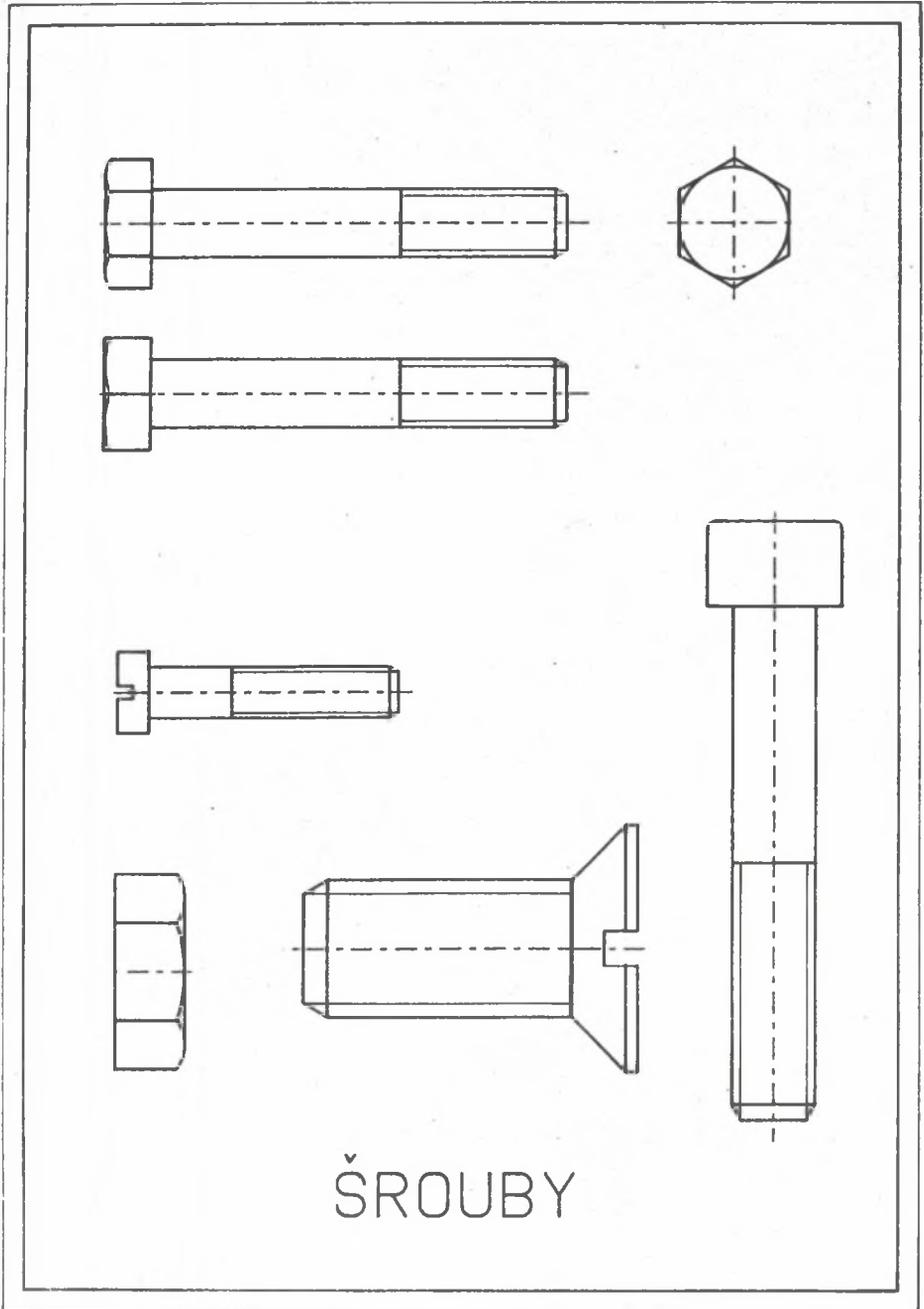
Parametrisch bearbeitete Normteile (Schrauben)
